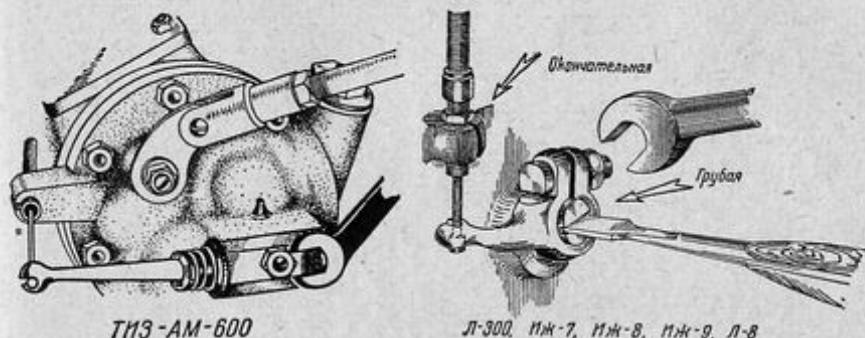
Регулировка величины хода выключения муфты сцепления.
